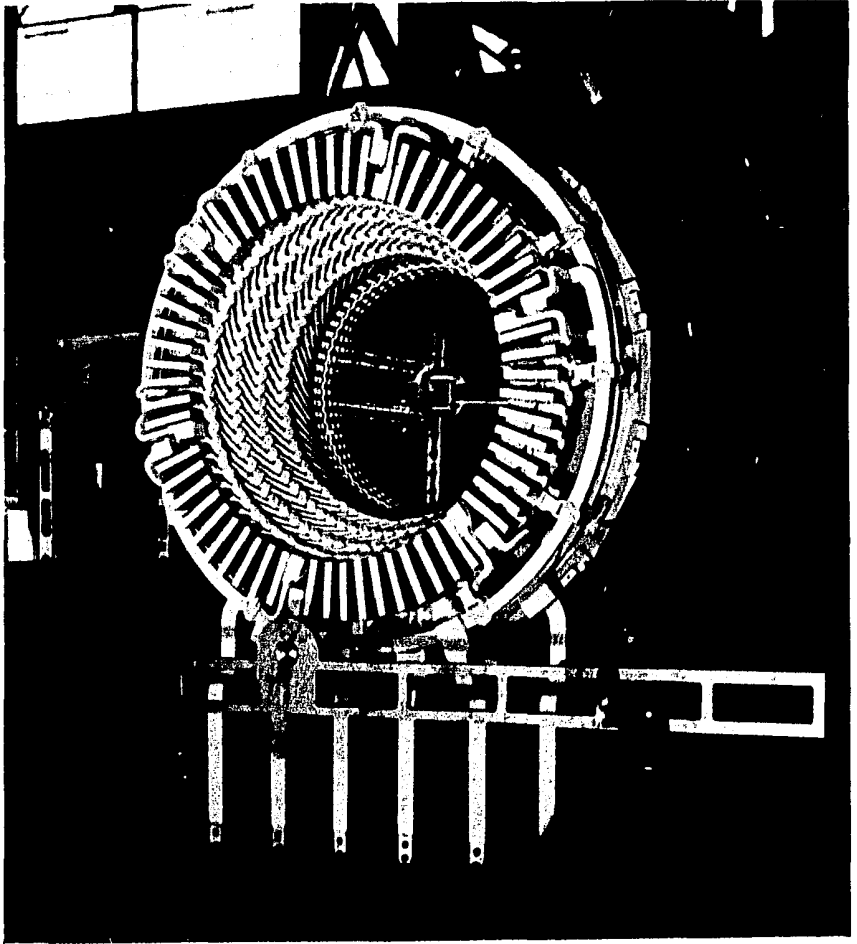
ESTATOR COMPLETAMENTE TERMINADO SIENDO INSER EN LA PARTE INFERIOR DEL SOPORTE
